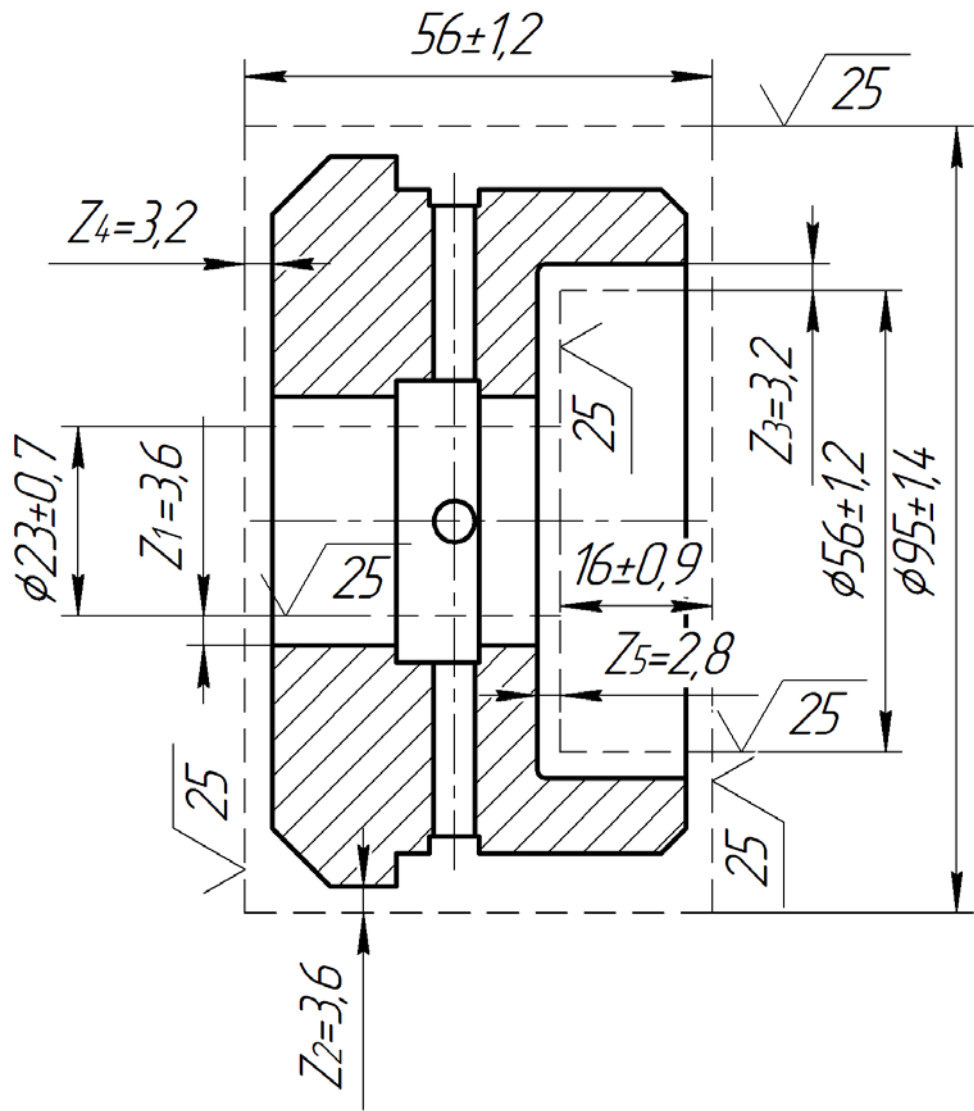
Заготовка Втулки ПМ-298.22.003.
